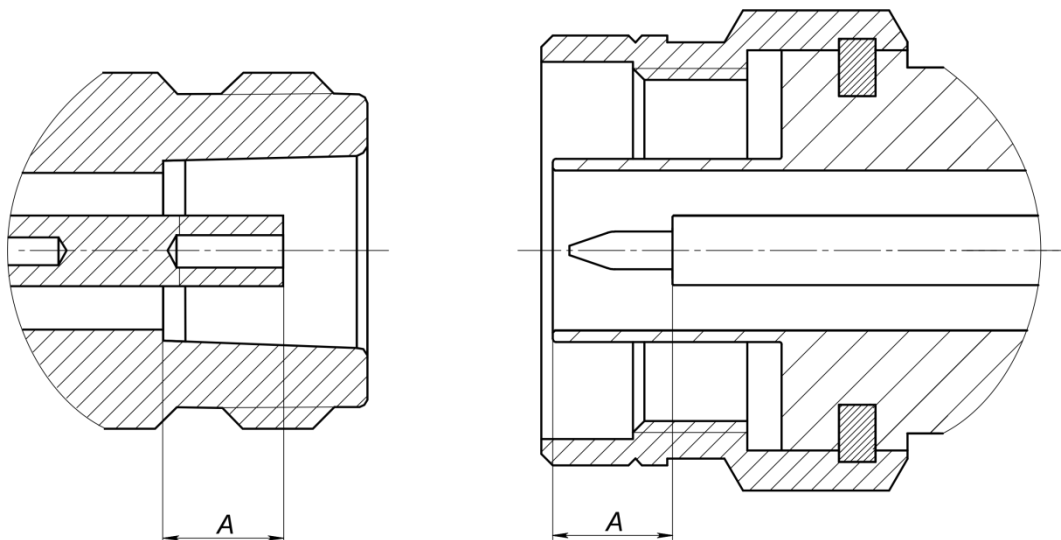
Соединители тип N и III (розетка и вилка)
